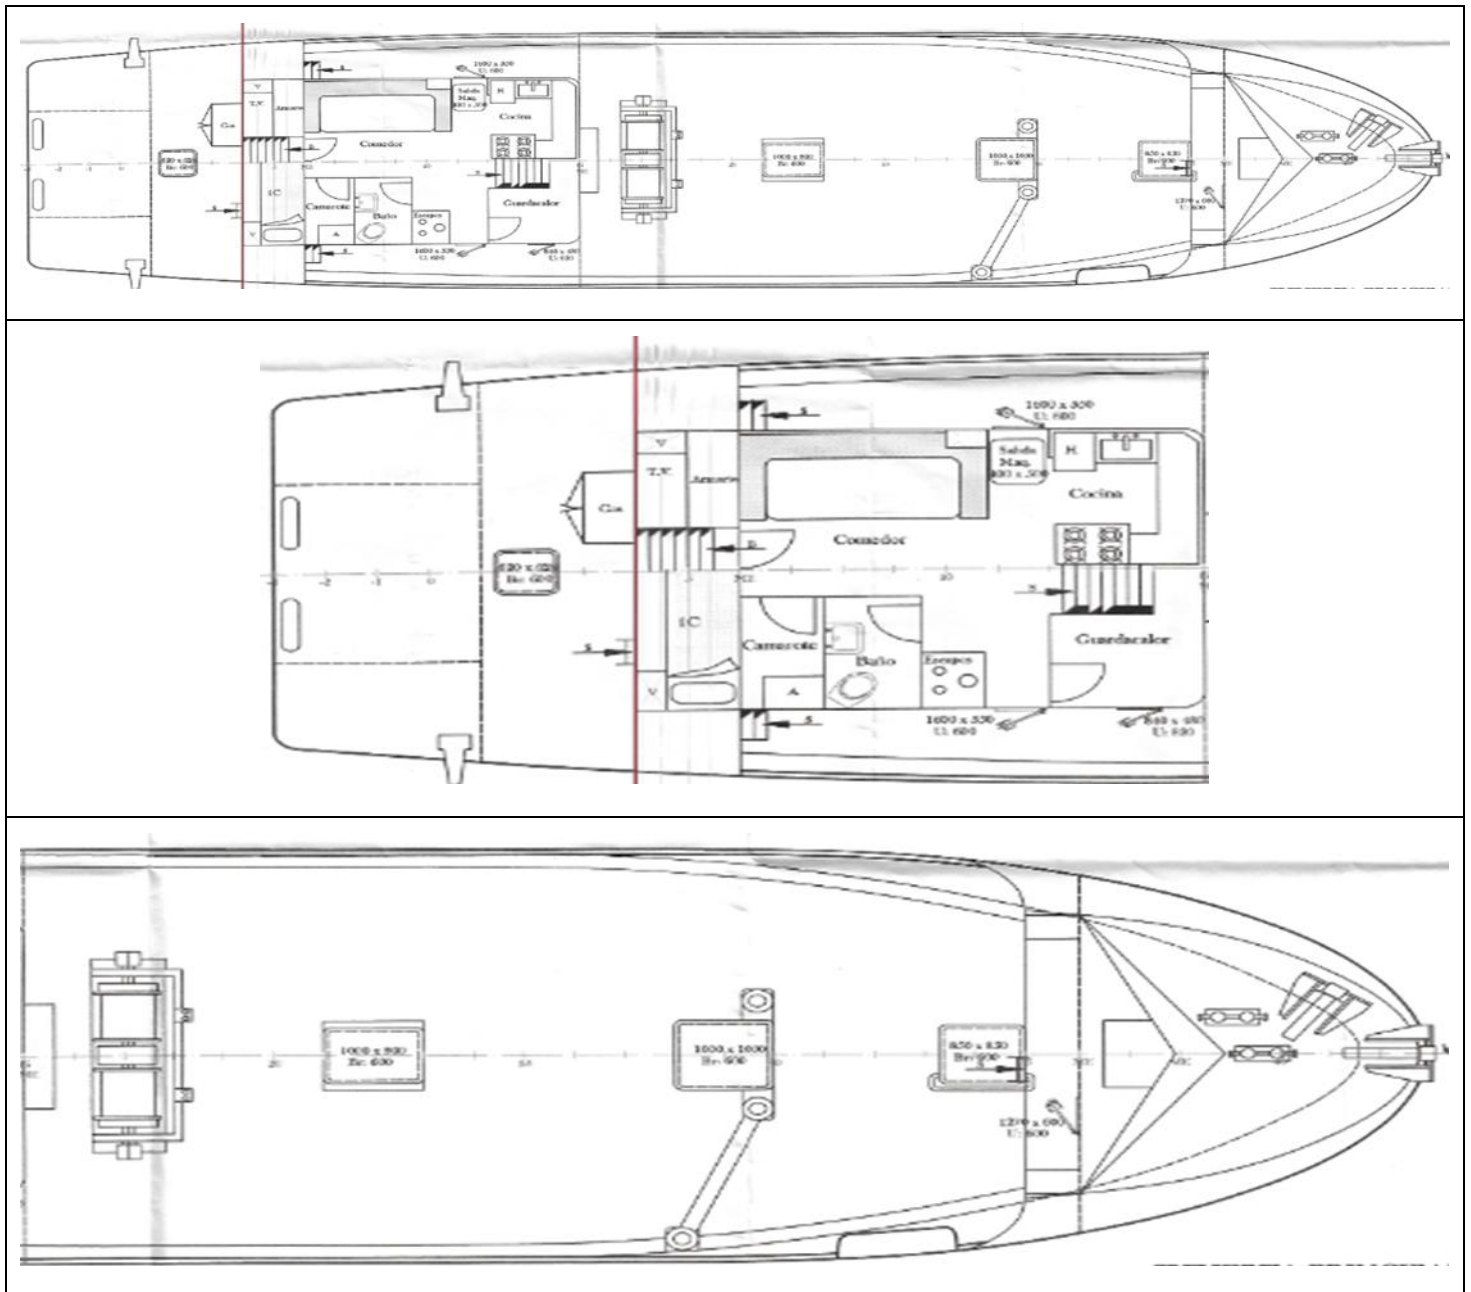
Plano de arreglo general de la cubierta principal del buque. Detalles a popa y a proa del casillaje.
